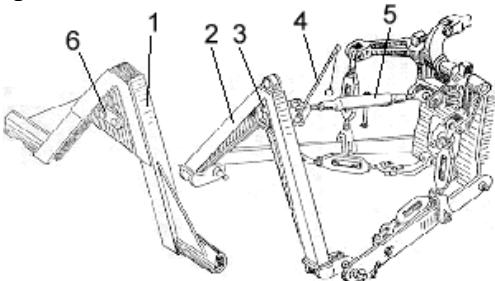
Механизм навески. 1-замок автосцепки; 2-автосцепка; 3-собачка; 4-трос; 5-верхняя центральная тяга; 6-планка регулировочная.
